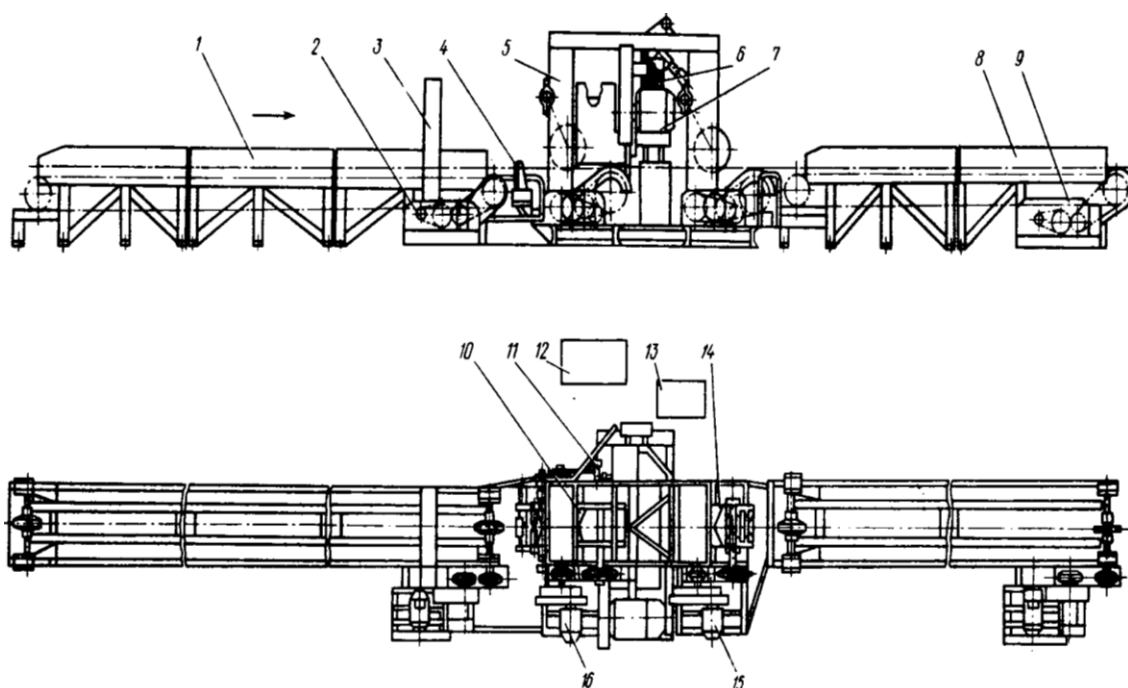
Схема станка ОК100-2: 1 – подающий конвейер; 2 – привод подающего конвейера; 3 – арка; 4 – шторка датчика подачи бревна; 5 – станина; 6 – окорочная головка; 7 – привод окорочной головки; 8 – приемный конвейер; 9 – привод приемного конвейера; 10 – подающая секция механизма подачи; 11 – система центрирования ротора; 12 – электрооборудование; 13 – гидросистема; 14 – приемная секция механизма подачи; 15, 16 – приводы приемной и подающей секций механизма подачи
